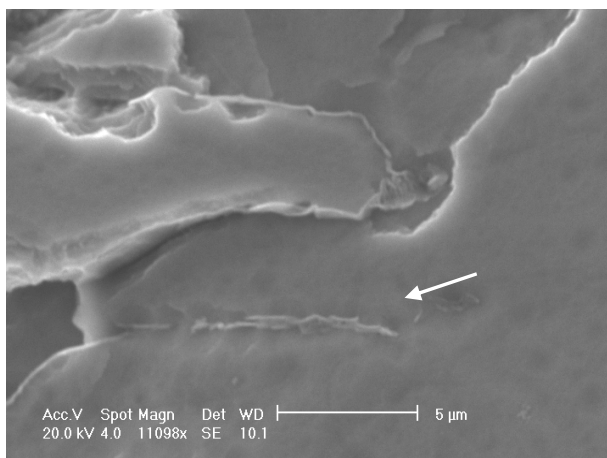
Detalle del Inicio principal de fractura producido por la rotura de un carburo.
